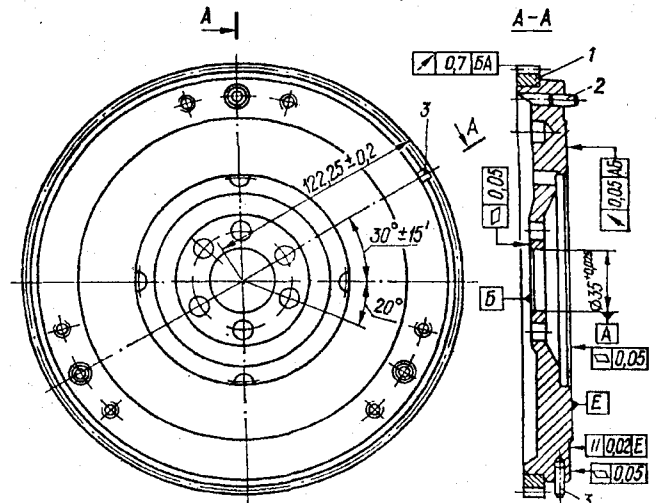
Маховик: 1 – обод маховика; 2 – штифты установки кожуха сцепления; 3 – штифт диагностический ВМТ
